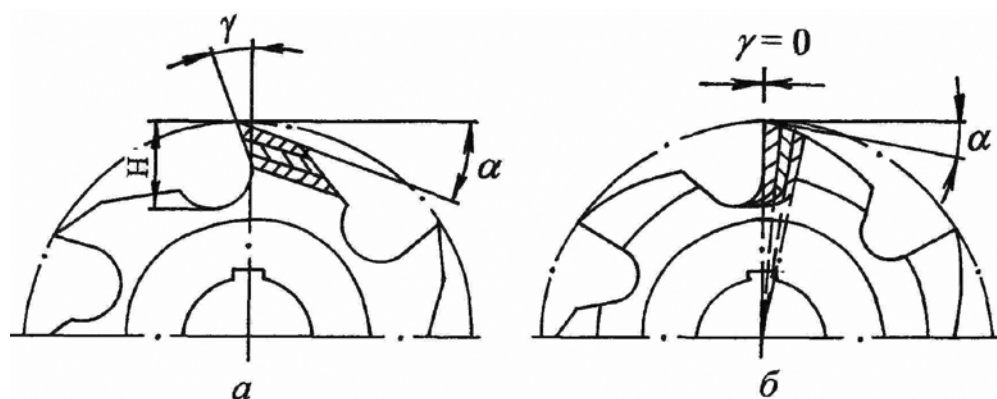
Формы профилей зубьев: *a* – остроконечные; *б* - затылованный
